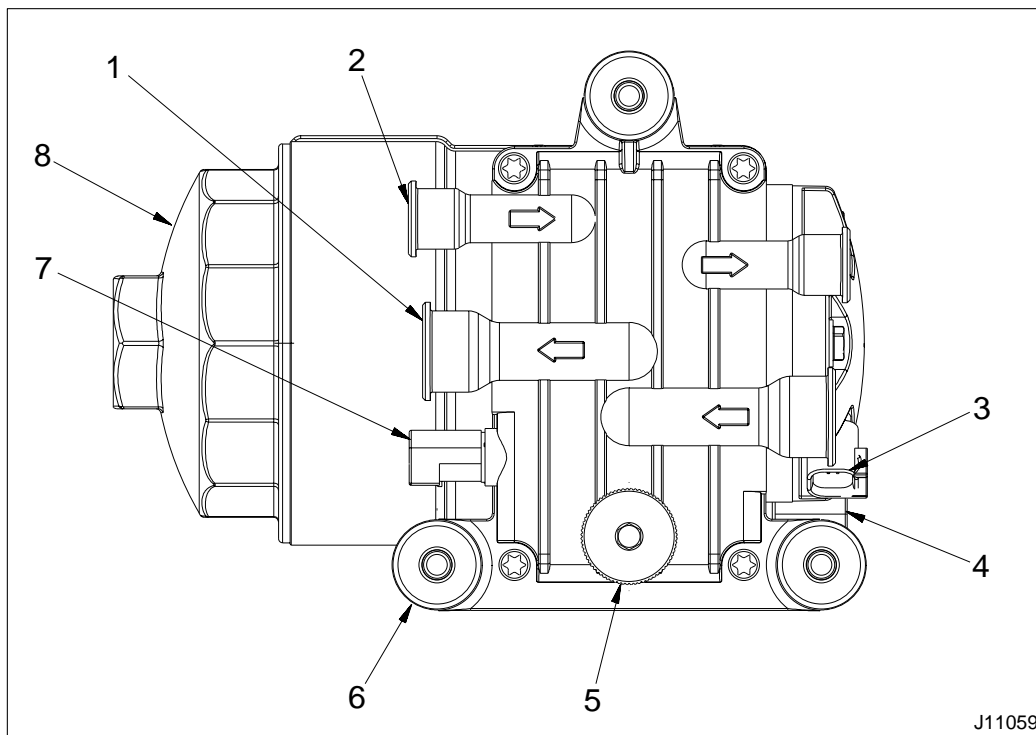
Módulo horizontal acondicionador (instalado en el chasis)
